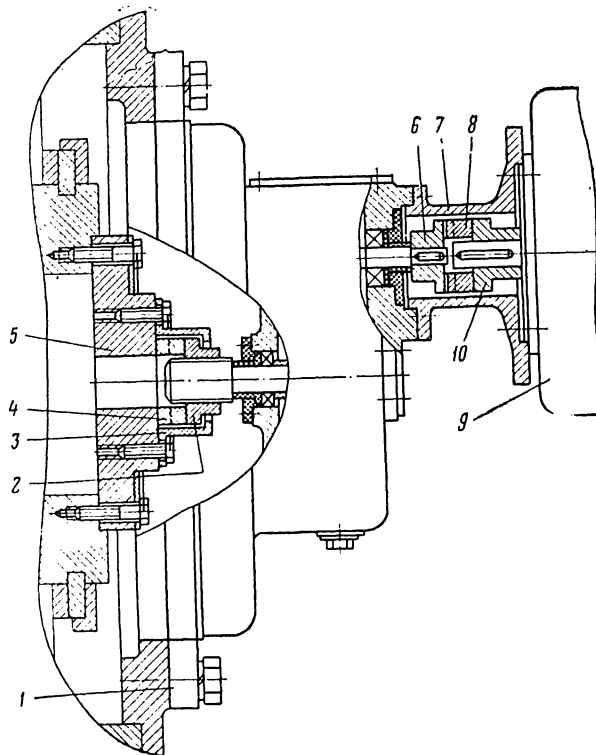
Установка тахогенератора с редуктором РВУ-100.
